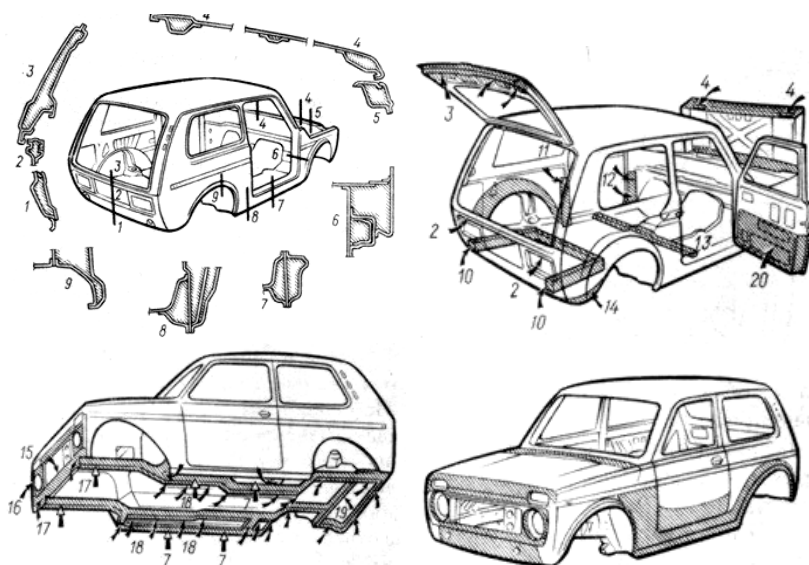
Места противокоррозионной обработки закрытых полостей кузова автомобиля ВАЗ-2121: 1 – нижняя поперечина панели задка; 2 – верхняя поперечина панели задка; 3 – полость двери задка; 4 – карманы капота; 5 – верхняя поперечина передка; 6 – карманы передних крыльев; 7 – полости порогов; 8 – полость между наружной и внутренней панелями боковины; 9 – полость между боковиной и аркой заднего колеса; 10 – полости задних лонжеронов; 11 – полости средних стоек; 12 – полости передних стоек; 13 – средняя поперечина пола; 14 – углубления за арками задних колес; 15 – нижняя поперечина передка; 16 – ниши фар; 17 – полости передних лонжеронов; 18 – полости лонжеронов пола; 19 – поперечина заднего пола; 20 – полости дверей; → – сверлить на кузове в сборе, а также имеющиеся технологические отверстия и доступные полости
